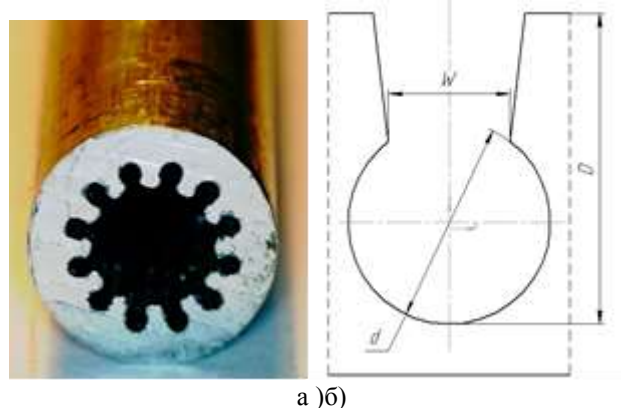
Загальний вигляд корпусу АКТТ (а) і поперечний переріз канавки (б)
